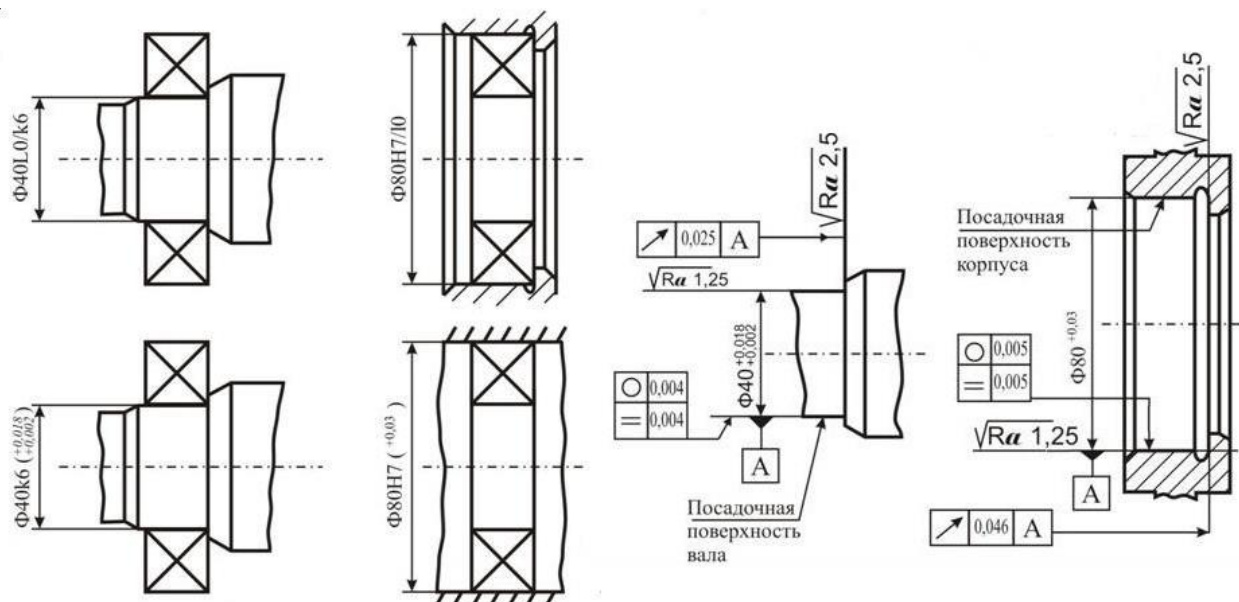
Обозначение посадок подшипника качения на сборочном чертеже(а) и требования к геометрическим параметрам посадочных поверхностей вала и отверстия корпуса под подшипник качения на рабочих чертежах (б)
